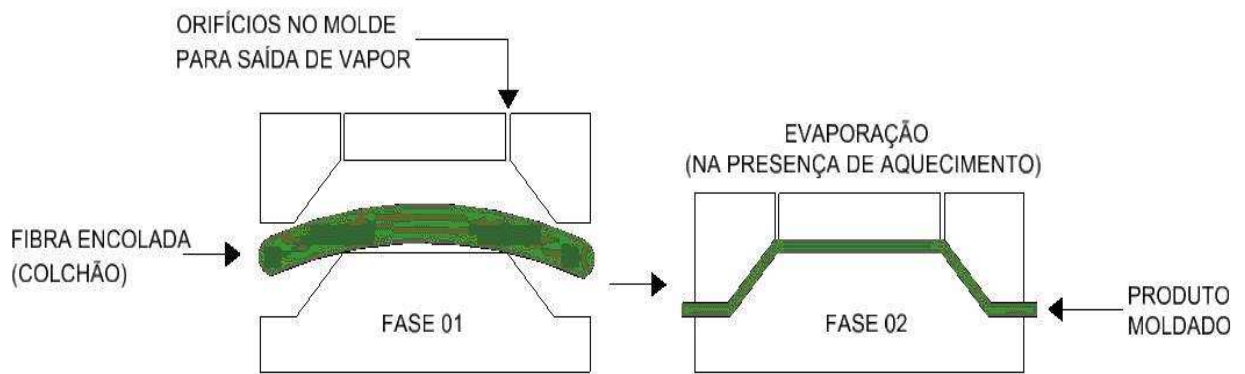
ESQUEMA DO PROCESSO DE MOLDAGEM A QUENTE
